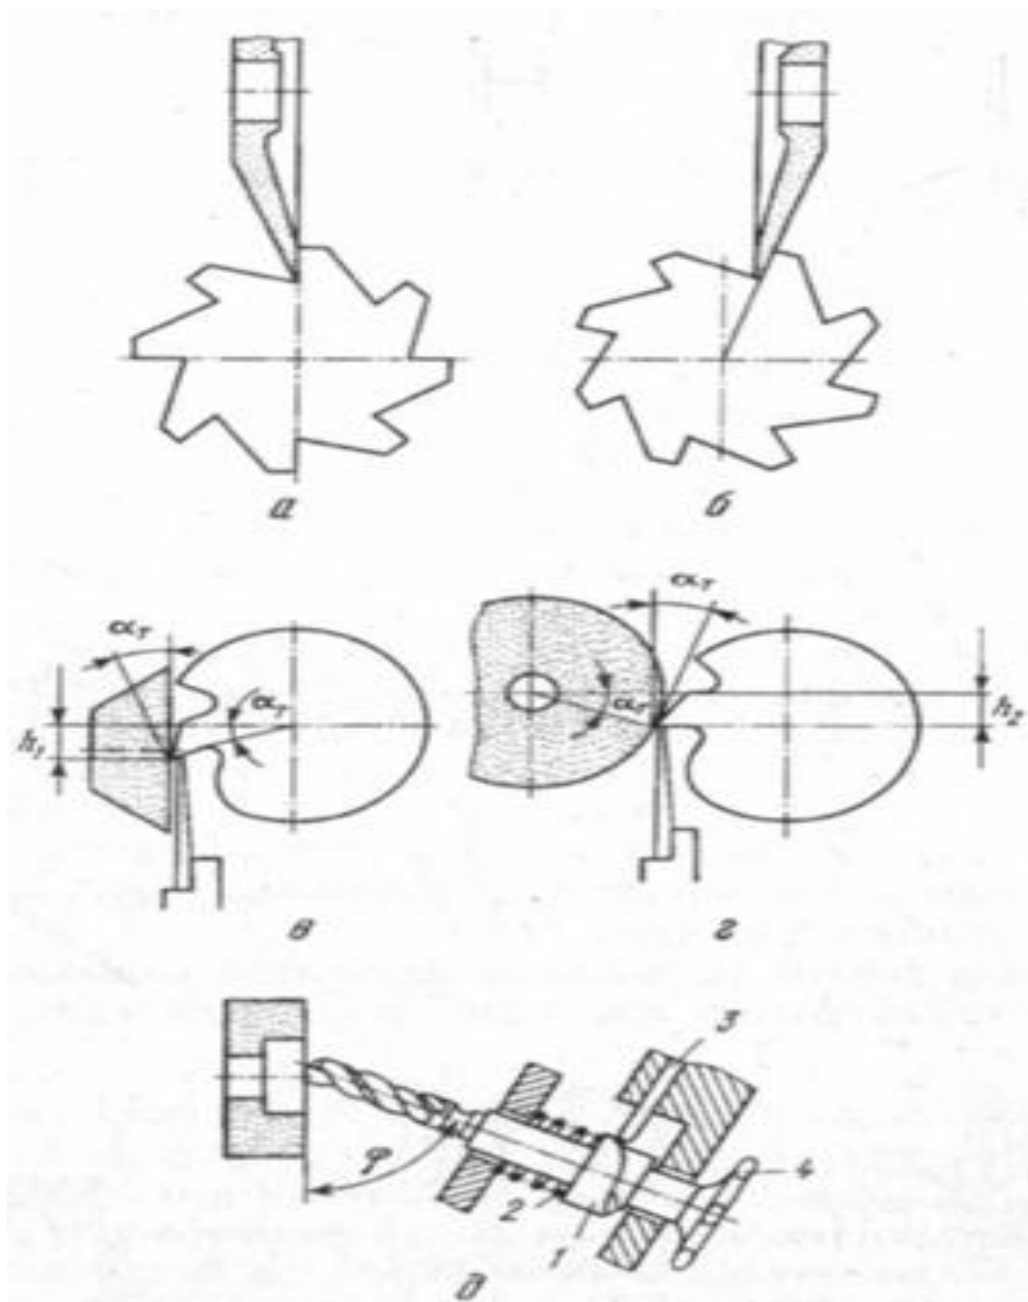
Схемы заточки поверхностей зубьев разверток и зенкоров: а – передних поверхностей инструмента с прямыми зубьями торцовой поверхностью тарельчатого круга, б – передних поверхностей инструмента с винтовыми или косыми зубьями конической поверхностью тарельчатого круга, в – задней поверхности на калибрующей части инструмента торцовой поверхностью чашечного круга, г - задней поверхности на калибрующей части инструмента периферией плоского круга, д – задней поверхности на режущей (заборной) части зенкера методом винтовой заточки, α_1 – задний угол в торцовом сечении, h_1 – величина установки вершины зуба относительно оси затачиваемого инструмента по схеме в, h_1 – величина смещения оси кру-
